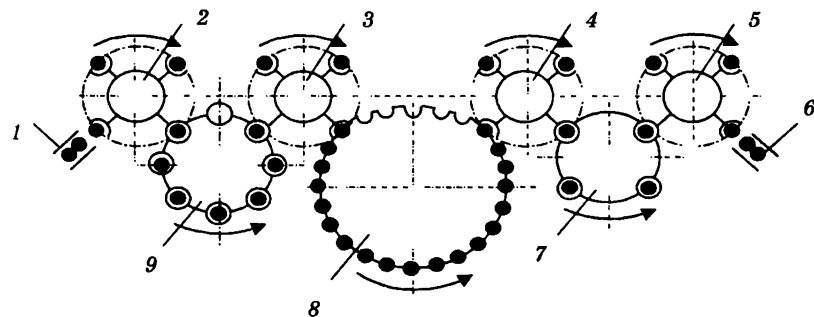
Схема роторної лінії: 1 — магазин-накопичувач; 2—5 — транспортні ротори; 6 — приймальний магазин; 7—9 — робочі ротори
